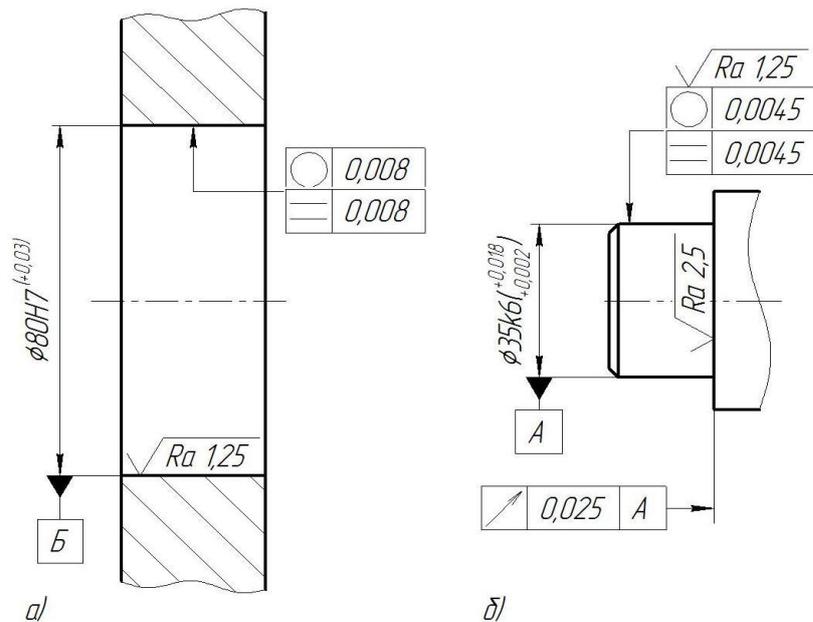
Примеры оформления технических требований сопряженных с подшипником деталей: а) корпус; б) вал
